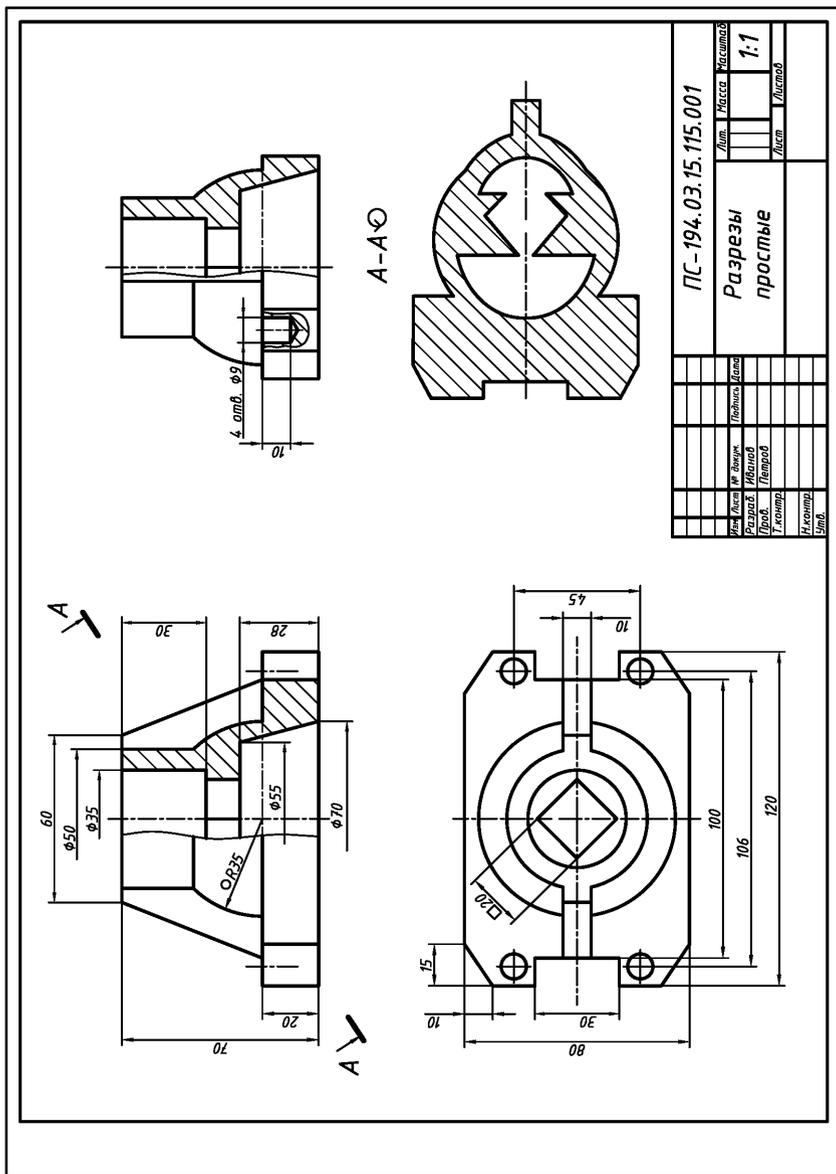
Пример оформления чертежа детали с двумя плоскостями симметрии (вариант исходной заготовки – рис. 1.26)
